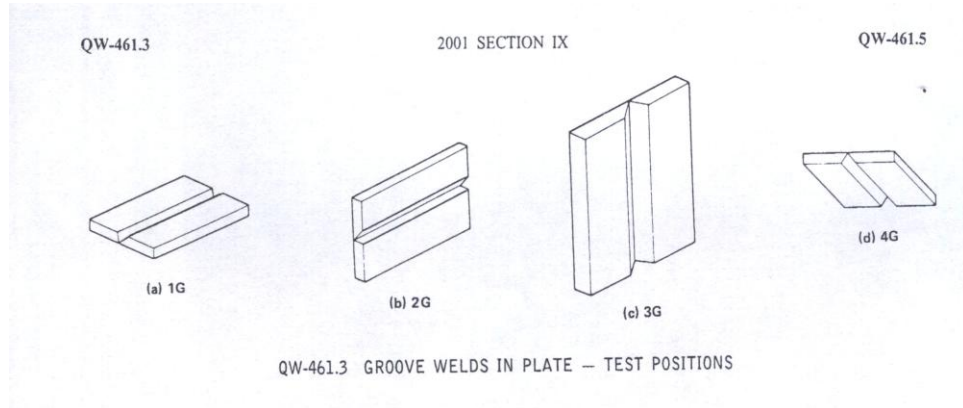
Posiciones de Soldadura según ASME
